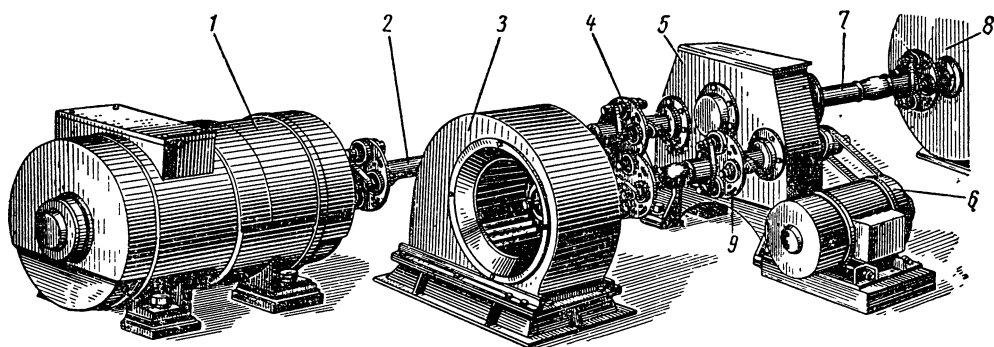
Общий вид привода от переднего редуктора (обозначения см. на рис. 176)
